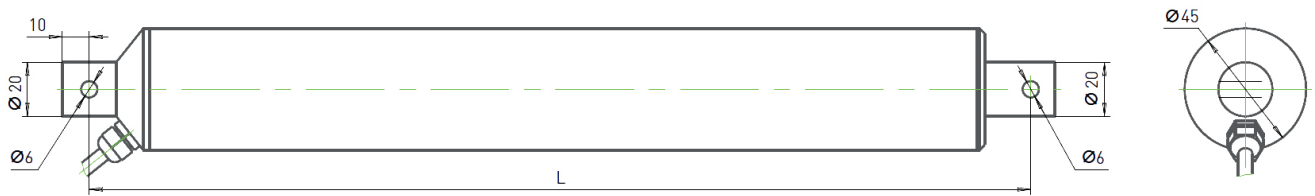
Габаритные и присоединительные размеры линейного актуатора
